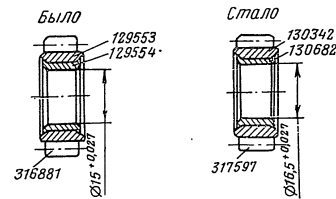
Валик редуктора двухскоростной передачи нагнетателя.
